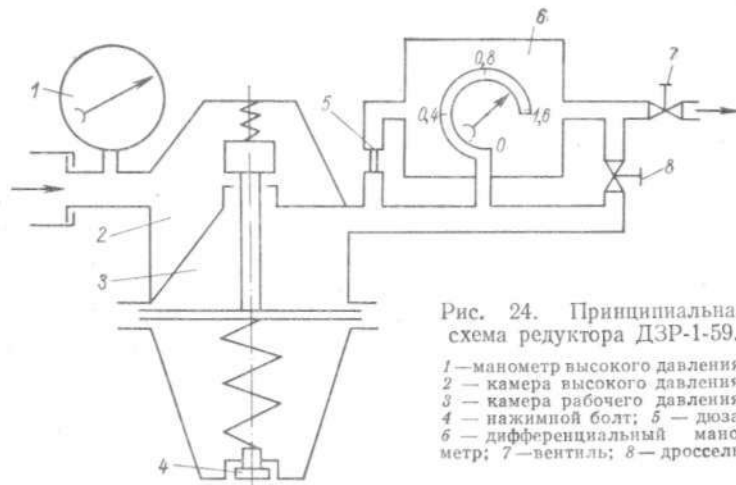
Принципиальная схема редуктора ДЗР-1-59.
